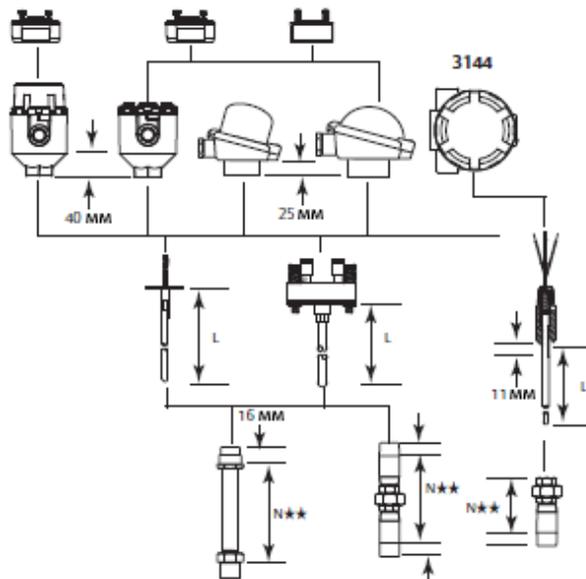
Габаритные размеры термопар ПП 65 и 185
